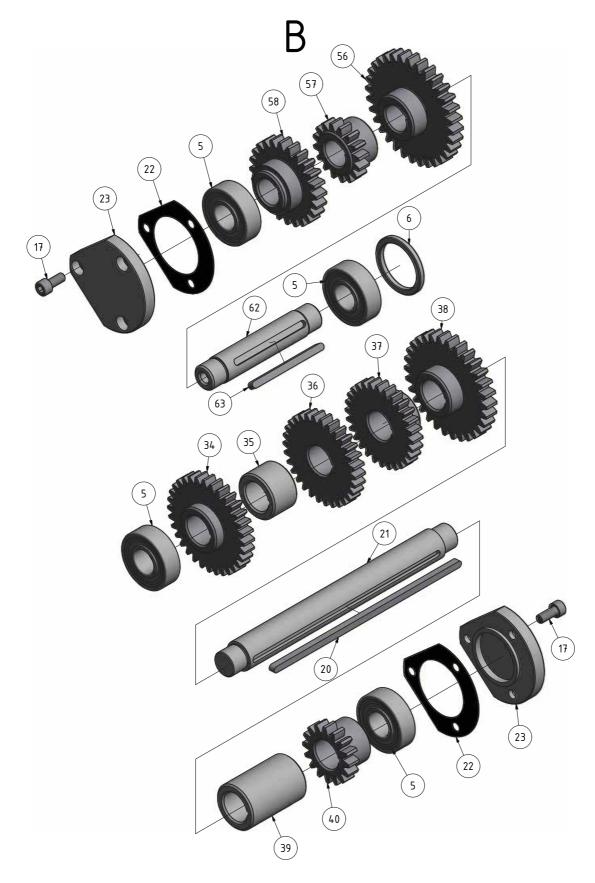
Vorschubgetriebe 4-6 - Feed gear 4-6
